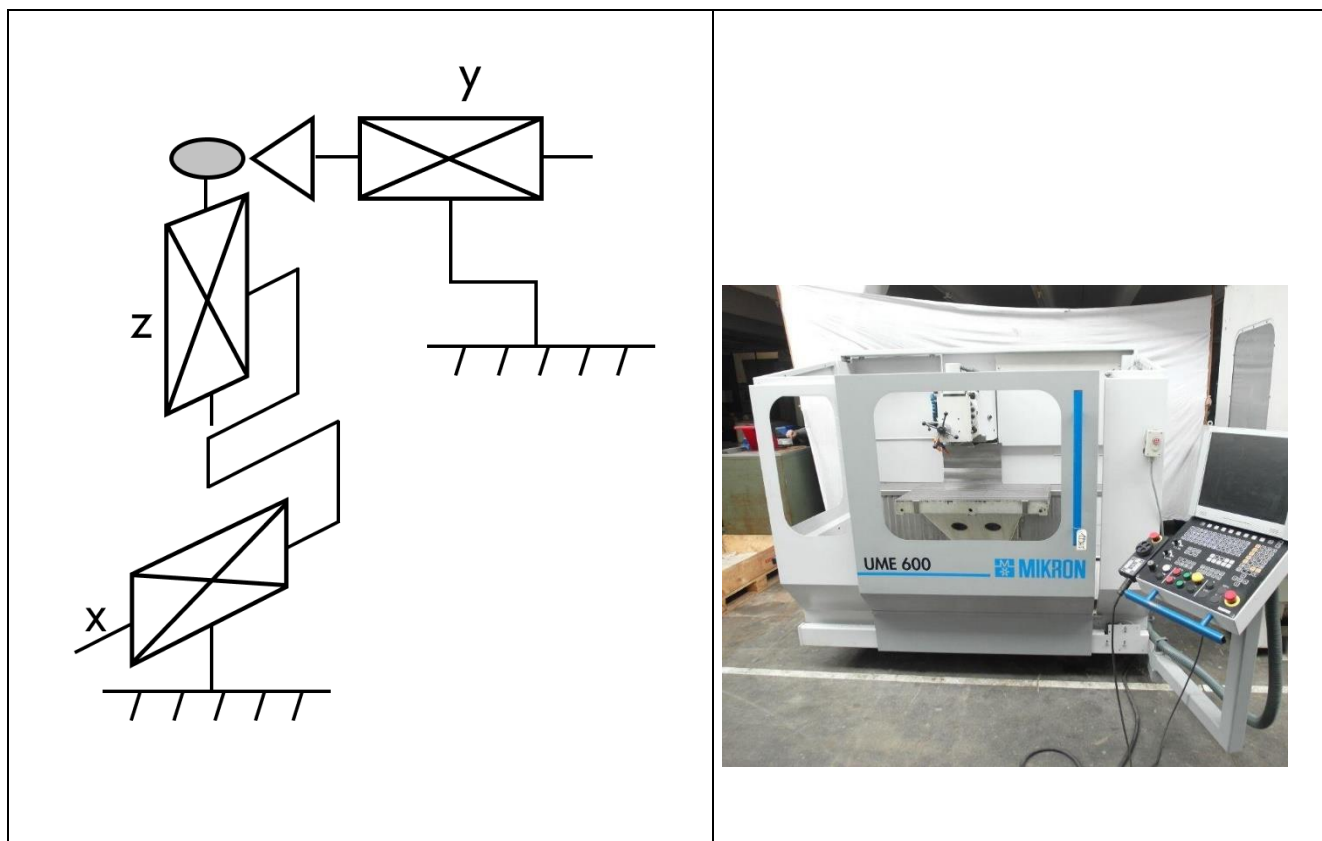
Универсально-фрезерный станок с ЧПУ Mikron UME 600 (Швейцария): слева – схема движения, справа – внешний вид
